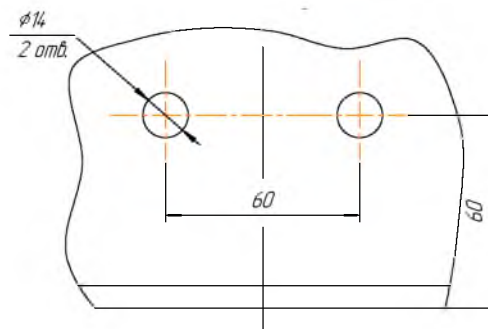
Разметка отверстий заземления полюсов к опорной конструкции
